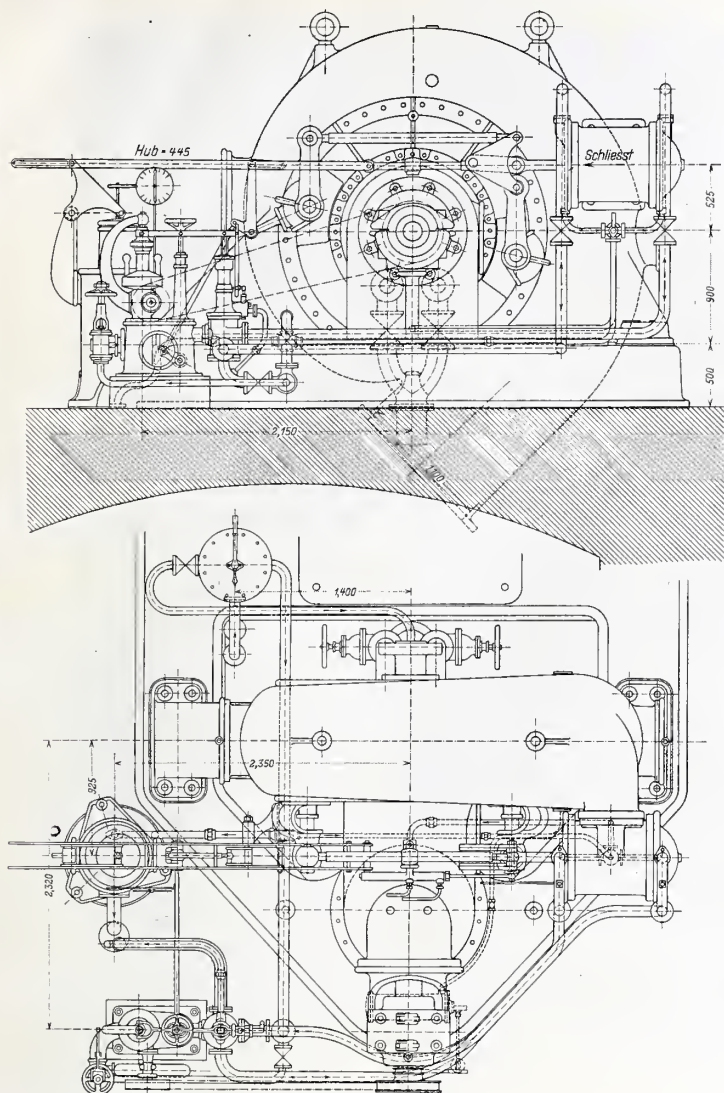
Vorderansicht, Seitenansicht und Grundriss
